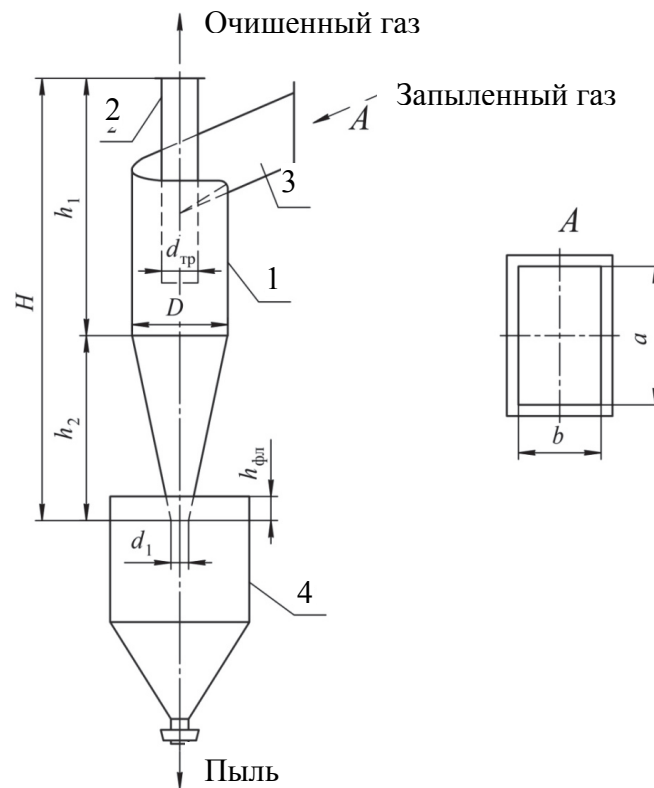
Схема циклона: 1 — корпус; 2 — труба; 3 — входной патрубок; 4 — приемный бункер
